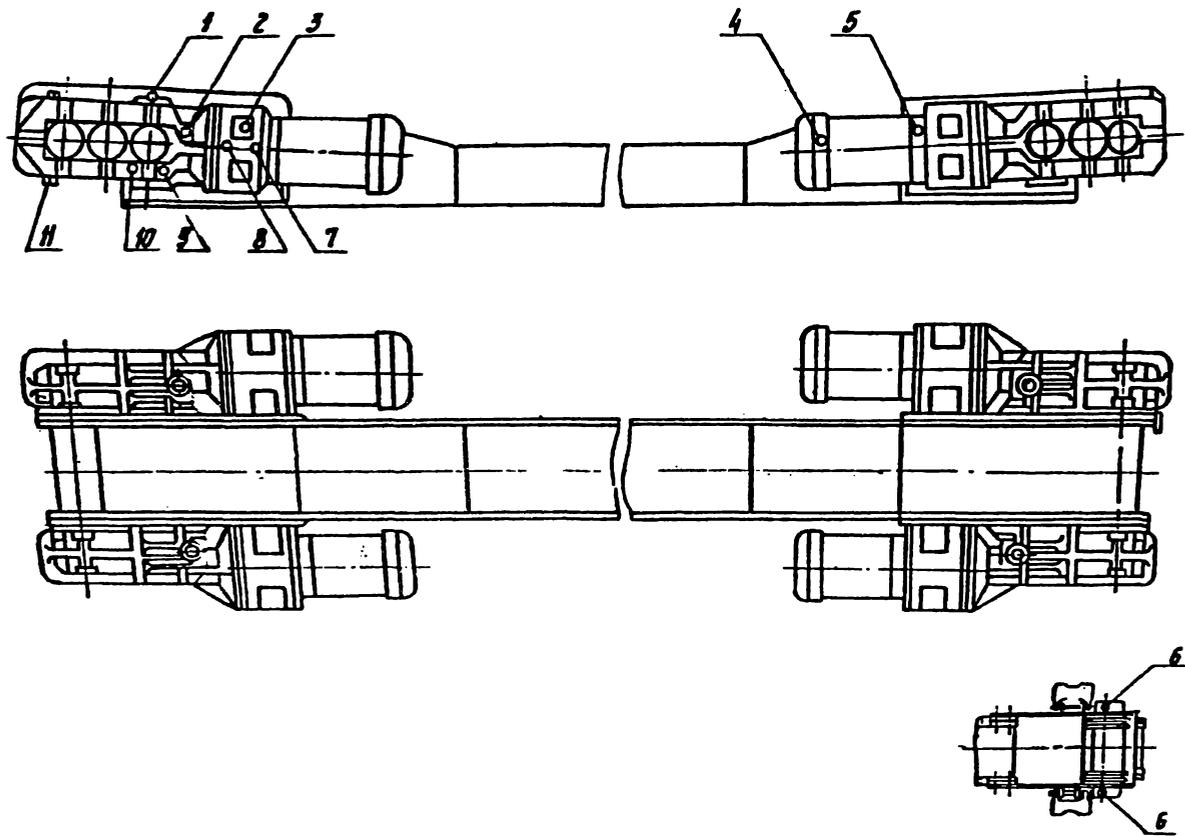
Схема смазки конвейера с двигателями мощностью 55 кВт
